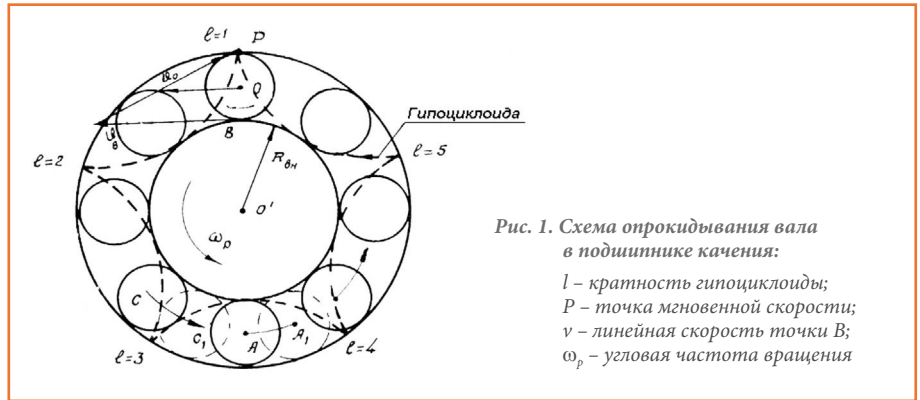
Схема опрокидывания вала в подшипнике качения:
